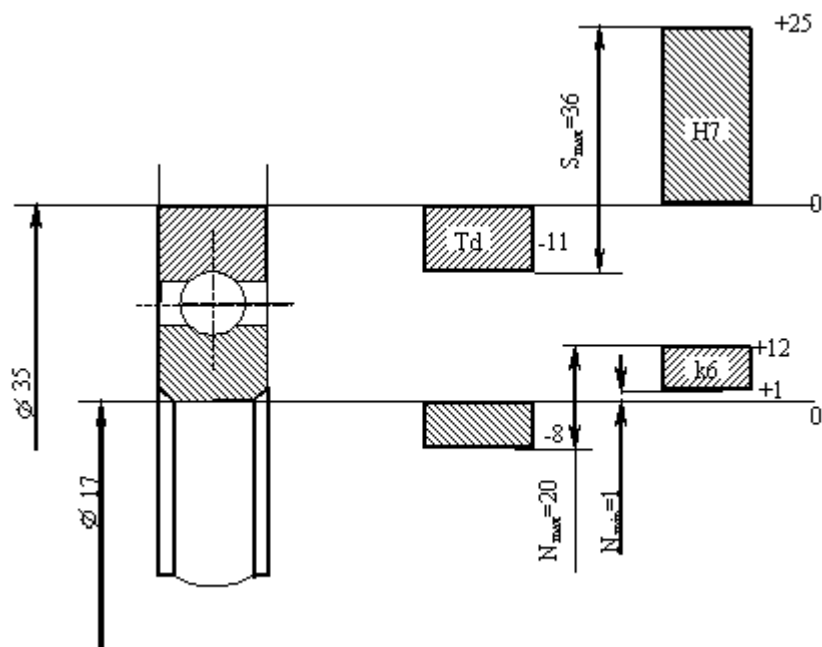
Схема расположения полей допусков колец подшипника качения, вала и отверстия в корпусе.
